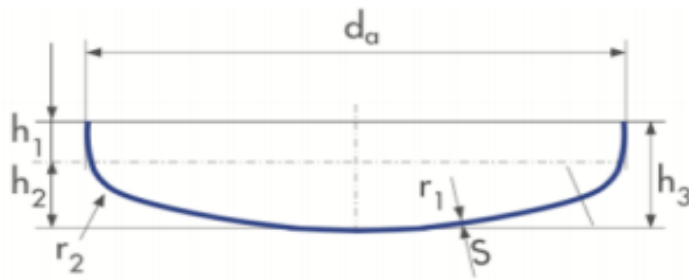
Muestra geometría de los cabezales y fondos
